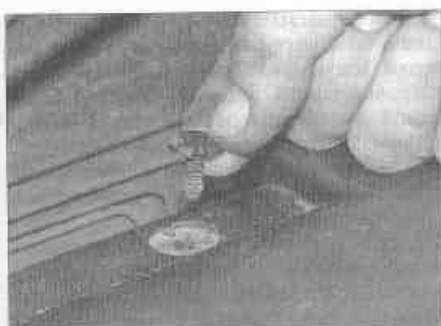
,б. ...извлеките пластмассовые фиксаторы в задней части крышки двигателя...
